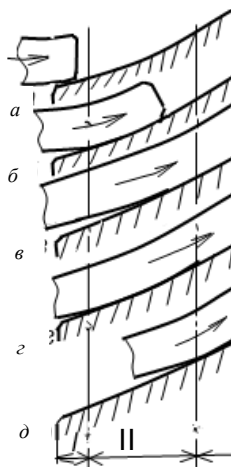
Схема процесса зацепления зубьев колеса с витком червяка классической глобоидной передачи [37]
